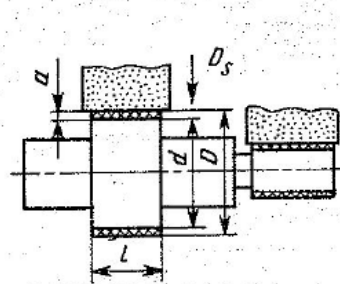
Схема наружного круглого шлифования методом продольной подачи напроход и в упор
